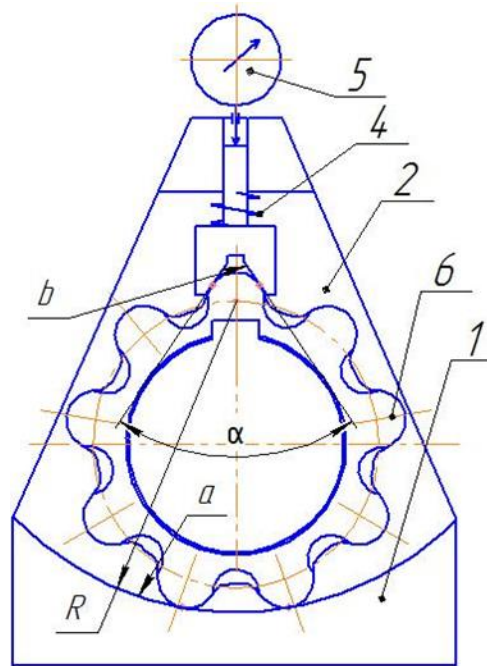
Схема пристрою для контролю зубчастого контуру внутрішнього ротора планетарного гідромотора
